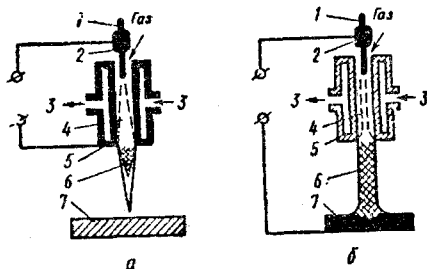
Плазменная сварка: а — плазмой, выделенной из столба дуги; б — плазмой, совпадающей со столбом дуги; 1 — вольфрамовый электрод; 2 — токоподводящий мундштук; 3 — охлаждающая вода; 4 — столб дуги; 5 — медное сопло; 6 — плазма; 7 — основной металл
